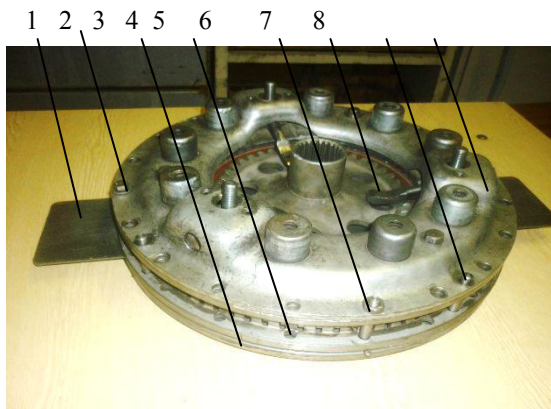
Главный фрикцион в сборе на кондукторе:
